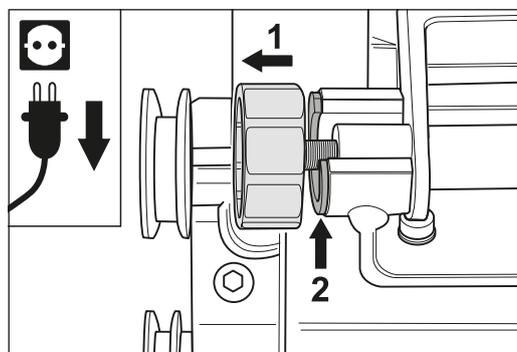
hasta que en ambas tuercas quede libremente visibles en la entrada en el bloque de rodamientos del motor.
